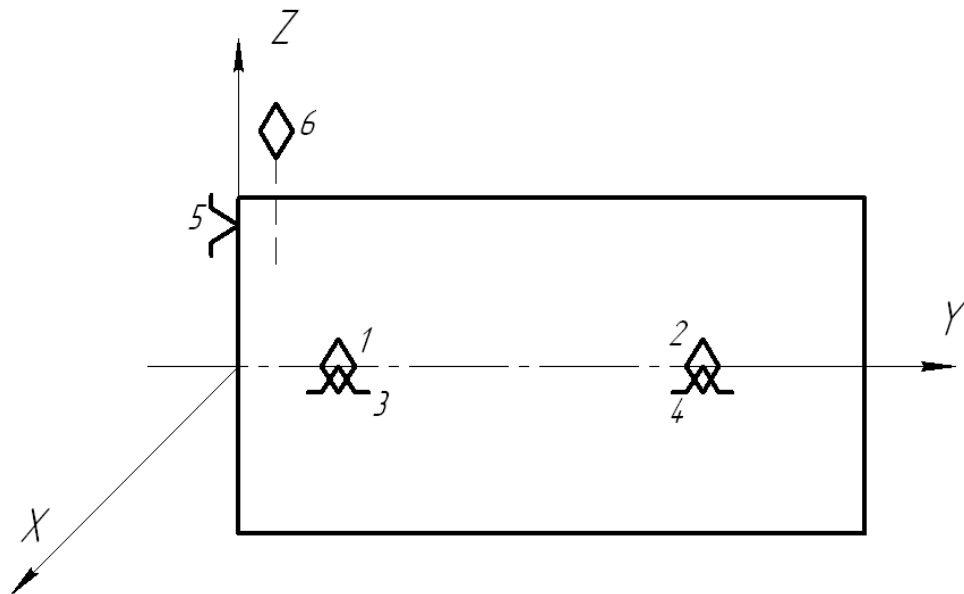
Схема базування для операцій 020, 025, 030, 055 в центрах
